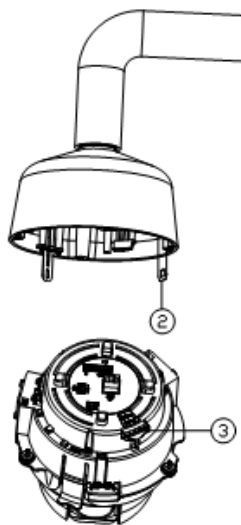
Подвесной монтаж в кабелепроводе/трубе
